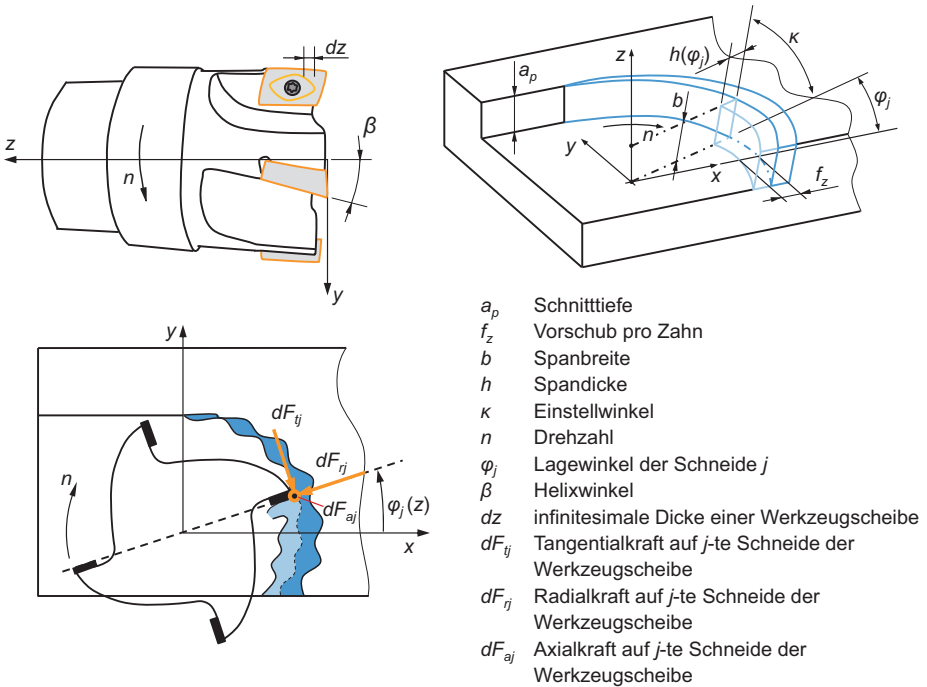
Geometrische Eigenschaften von Werkzeug und Werkstück
